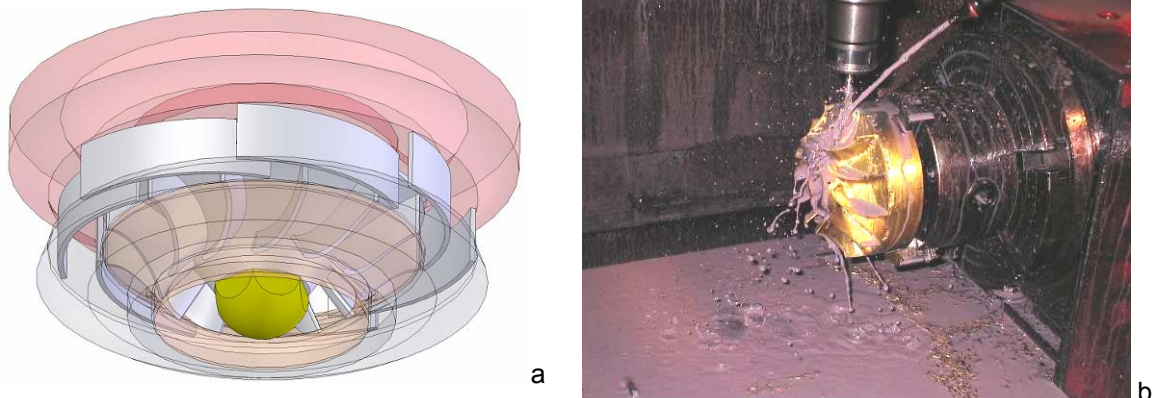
a) Diseño de la máquina hidráulica b) mecanizado del rotor en CNC.
